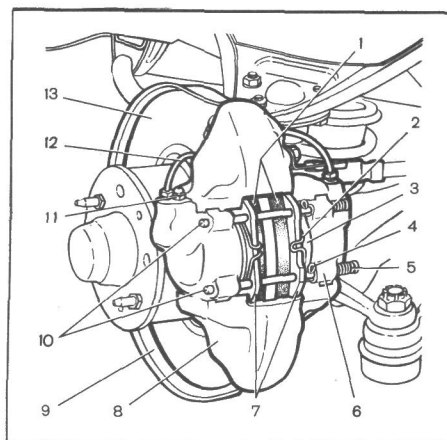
Передний дисковый тормоз: 1 — тормозные накладки; 2 — пружина; 3 — поршень тормозного цилиндра; 4 — шпилька; 5 — пружина; 6 — тормозной цилиндр; 7 — тормозные колодки; 8 — суппорт; 9 — кожух тормозного диска; 10 — пальцы крепления тормозных колодок; 11 — штуцер; 12 — соединительная трубка; 13 — тормозной диск
